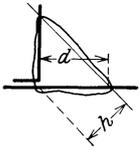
Nahtstärke bei Kehlschweißung.
